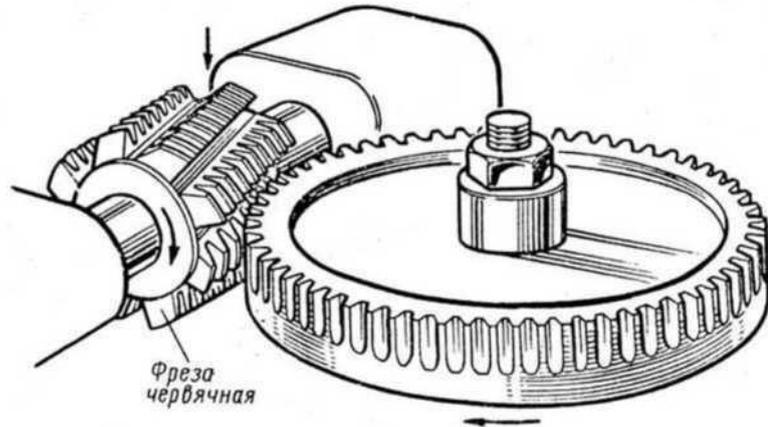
Схема фрезерування черв'ячної модульної фрезою
